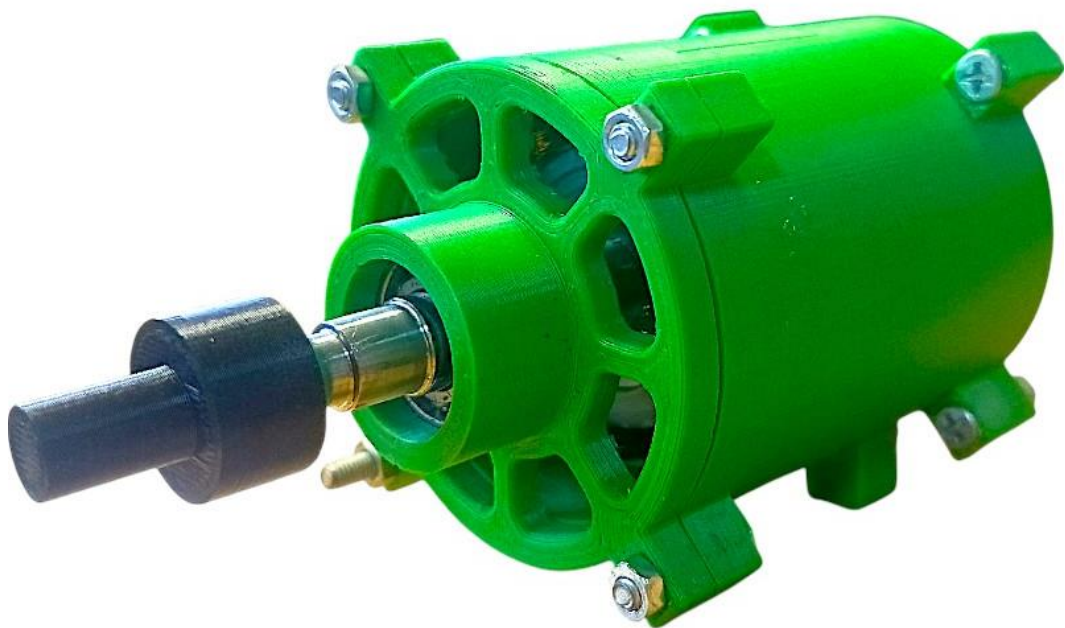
Макетный образец электродвигателя в сборе
